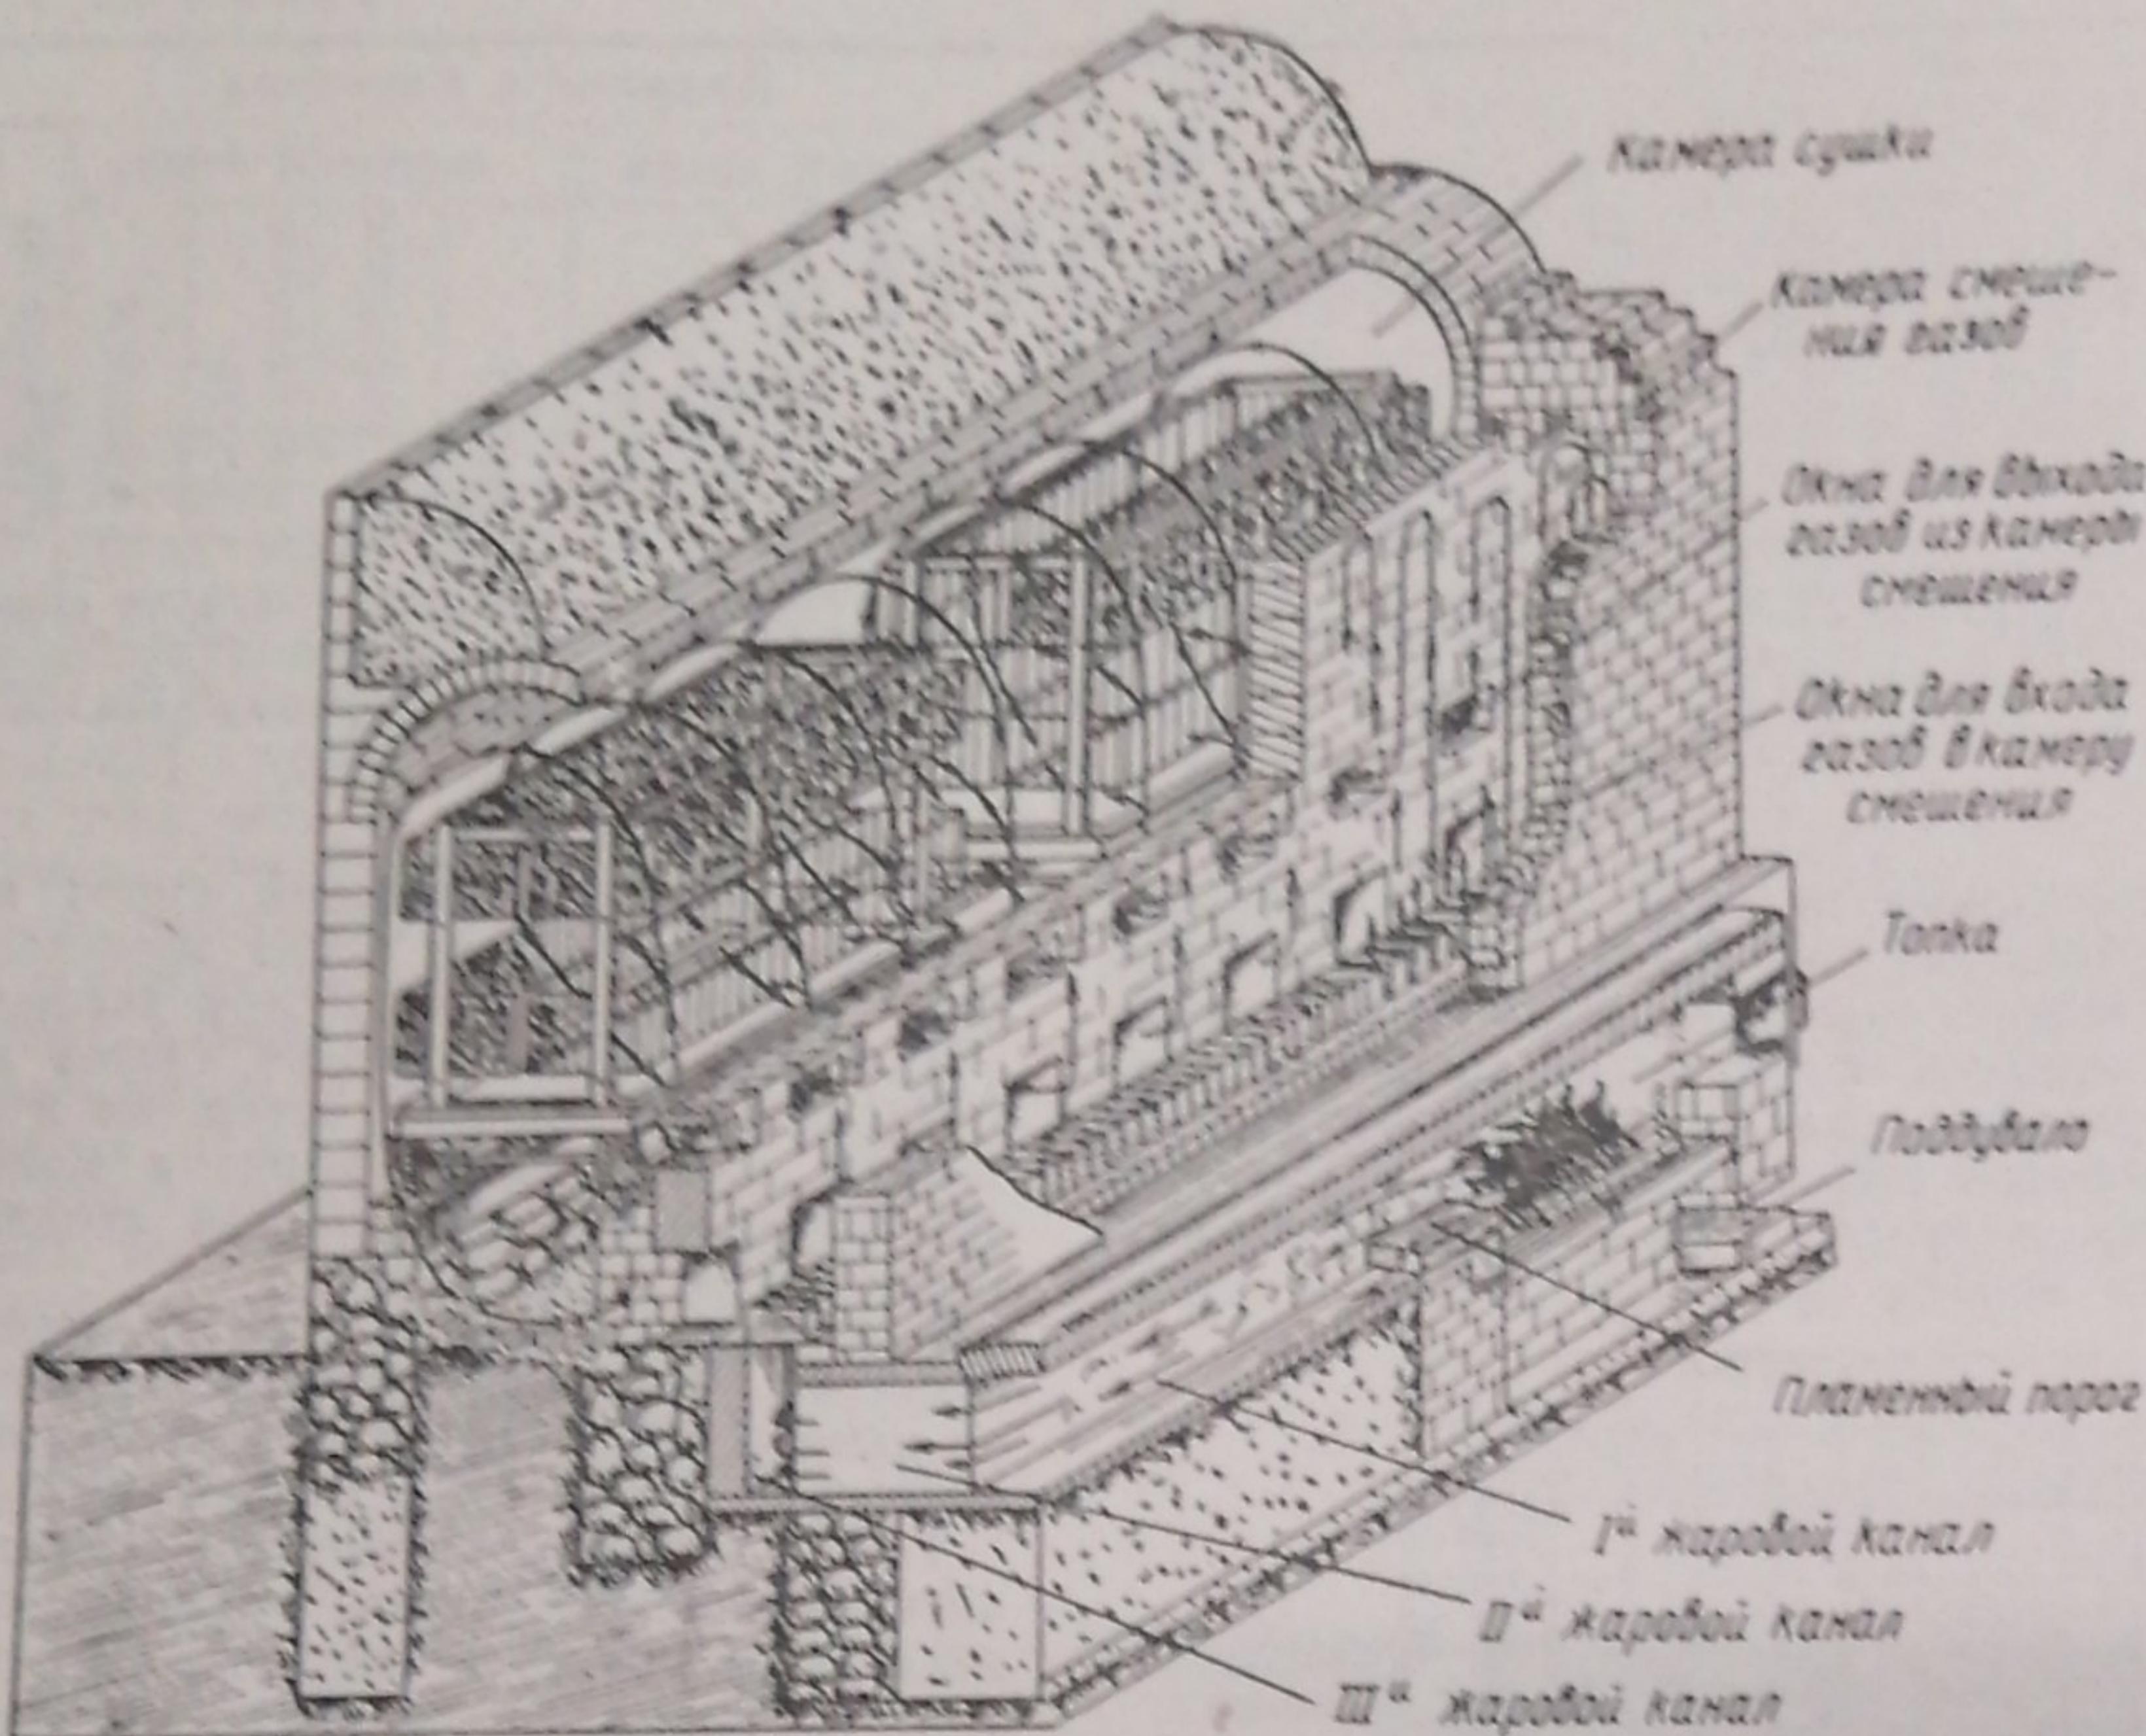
Схема движения газов в сушилке ЦНИИМЭ-9
